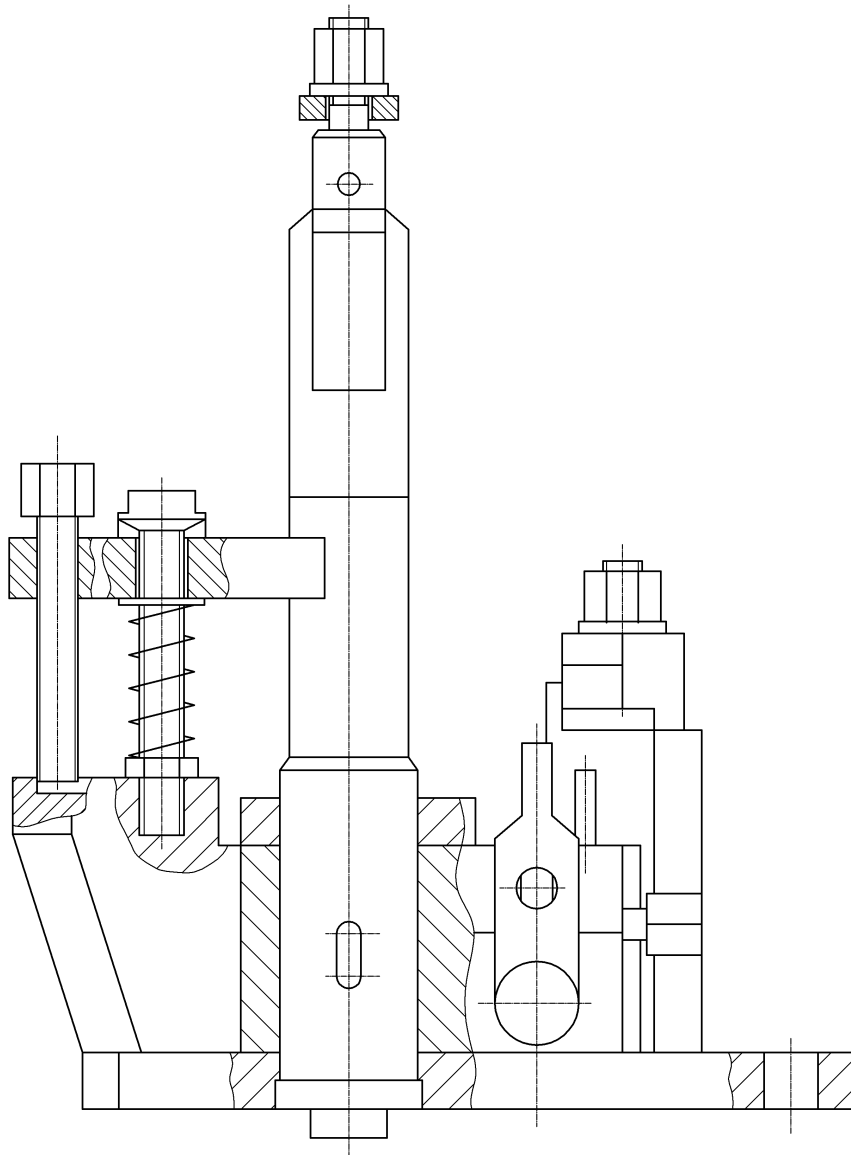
Установочний пристрій для обробки корпусу
